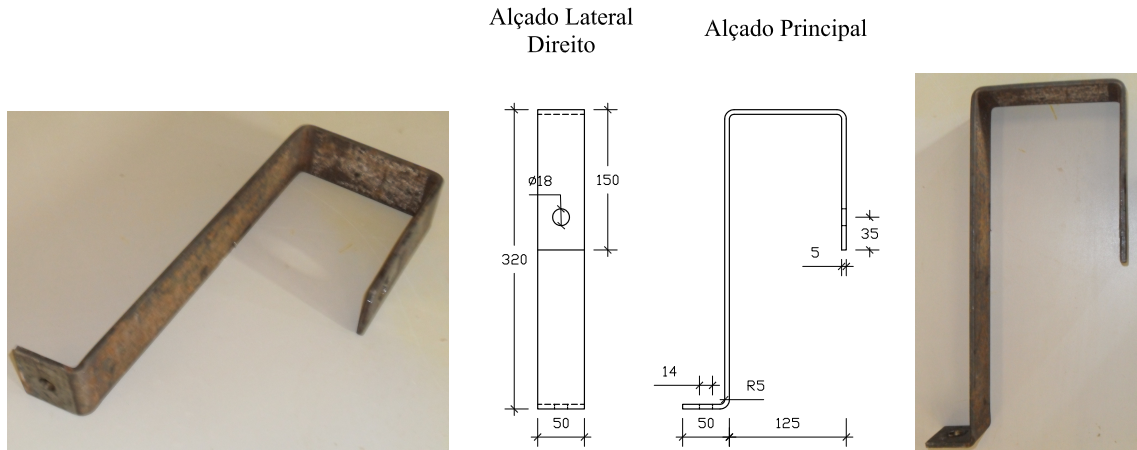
Vistas e dimensões do dispositivo DR 50x5 (mm)
